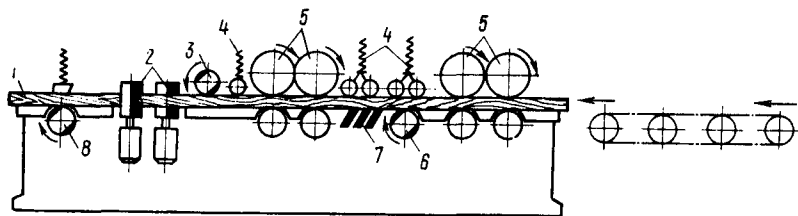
Схема четырехстороннего продольно-фрезерного станка:
